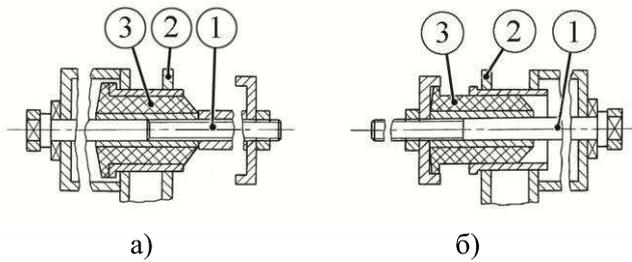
Схема выпрессовки и запрессовки шарнира рычага задней подвески:
